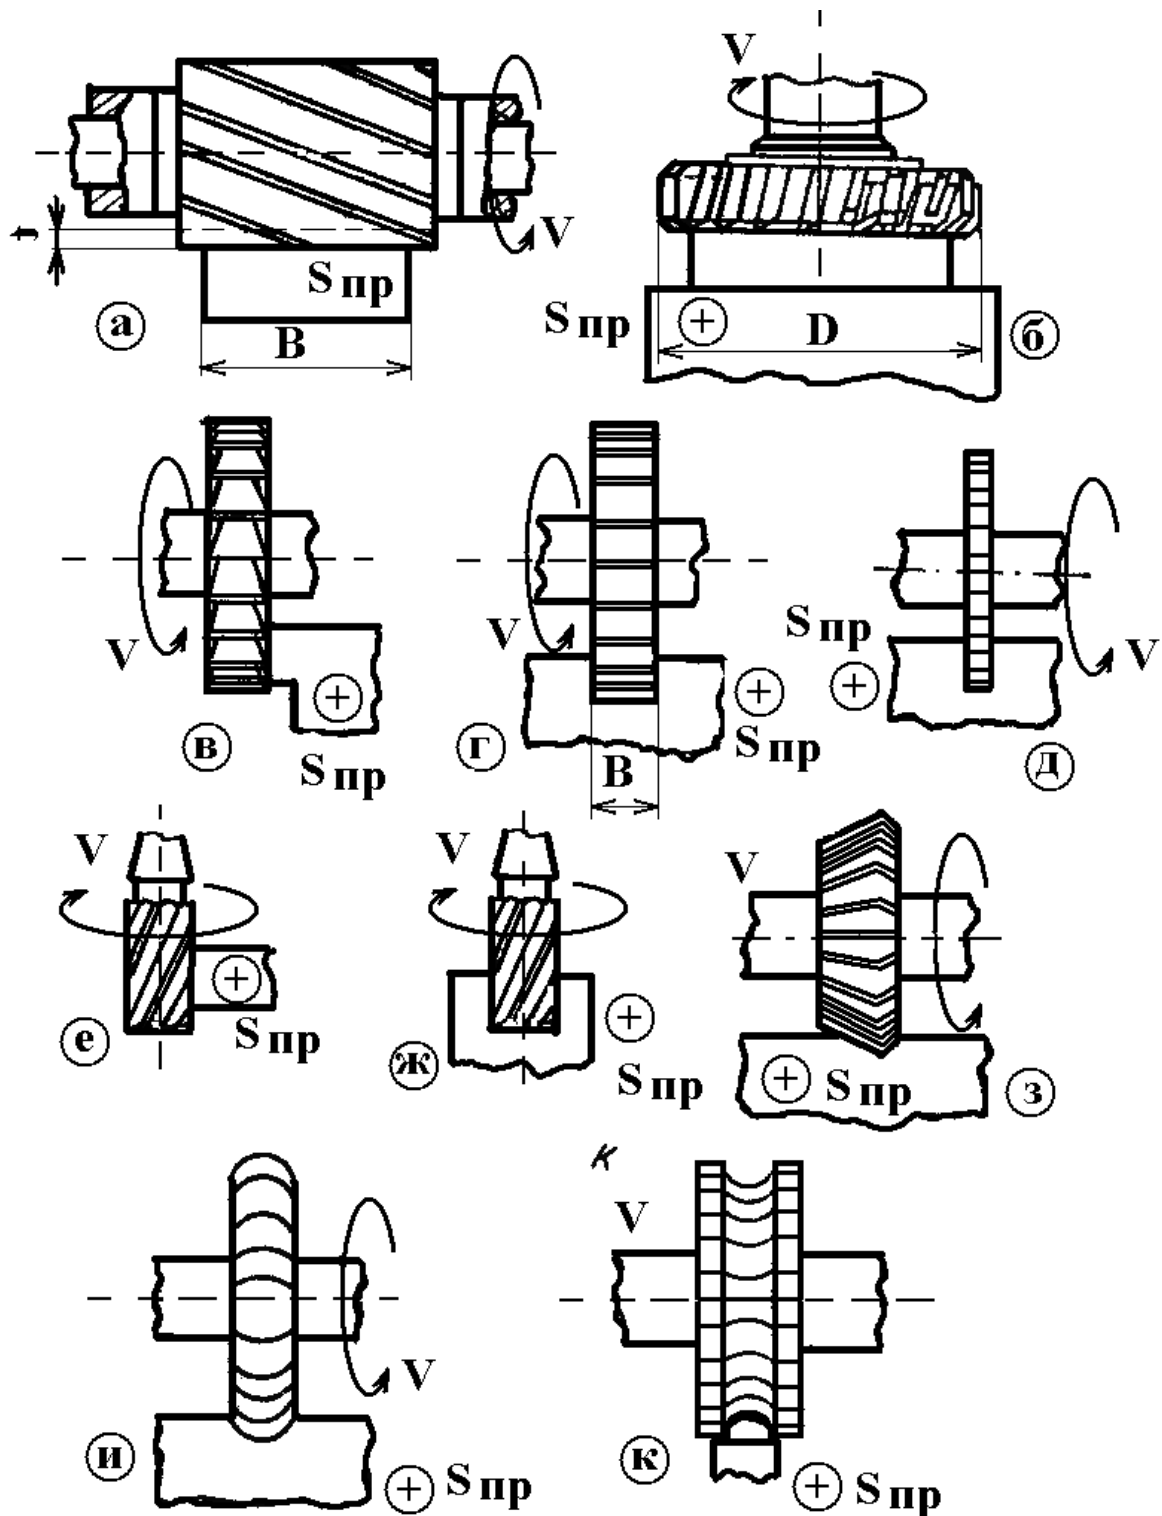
Типовые схемы обработки на фрезерных станках:
